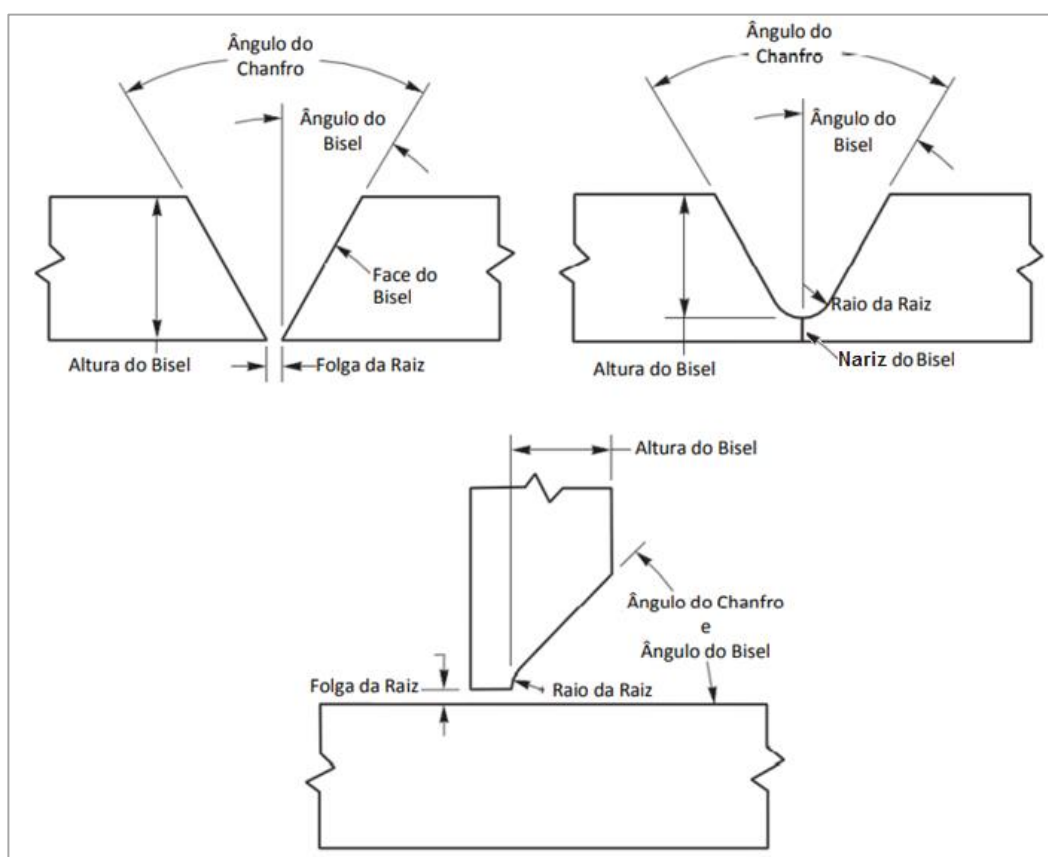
Principal nomenclatura utilizada numa junta de soldadura [14]
